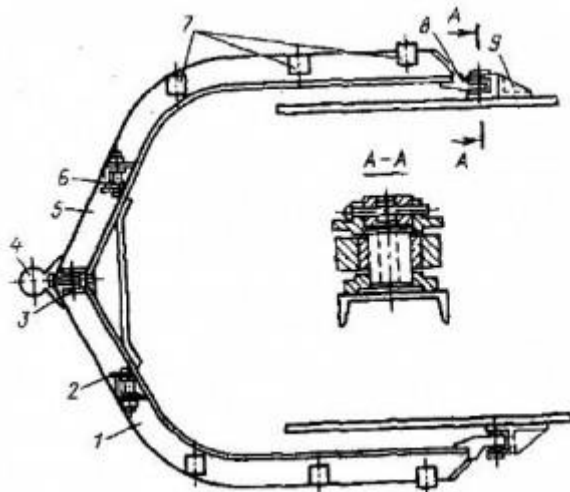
Универсальная толкающая рама: 1 и 5 — балки коробчатого сечения; 2, 3 и 6 — проушины с пальцами для крепления толкателей и раскосов; 4 — шарообразная головка рамы; 7 — проушины для присоединения толкателей; 8 — разрезные проушины для присоединения рамы к трактору; 9 — опоры тележек тракторов
